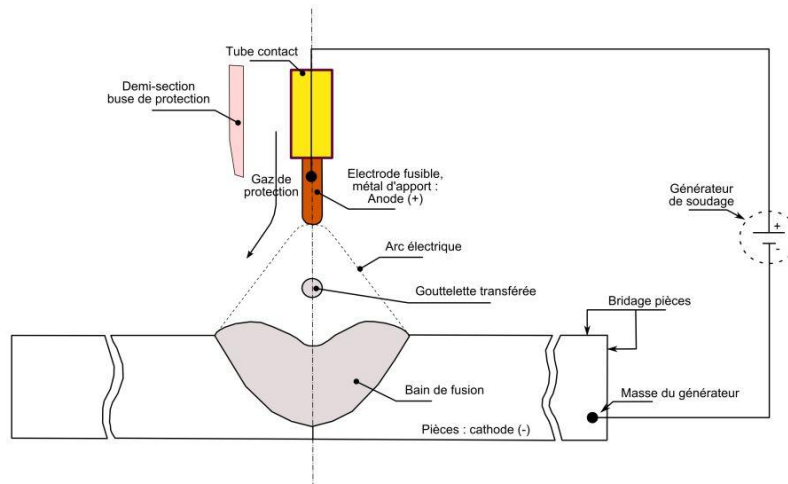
Principe du soudage MIG-MAG
